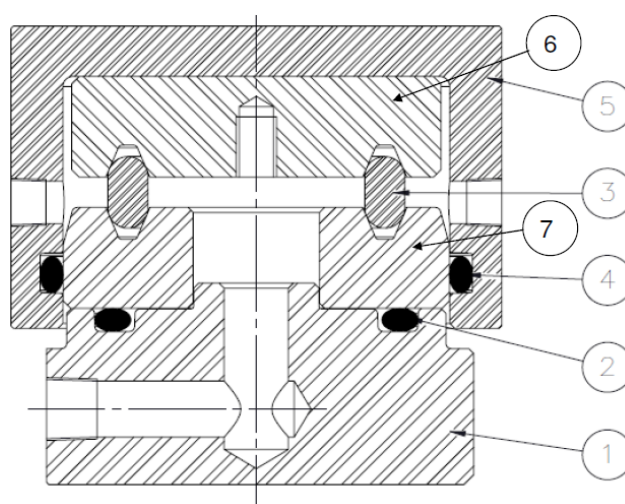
Desenho em corte do dispositivo de testes de vedação.
